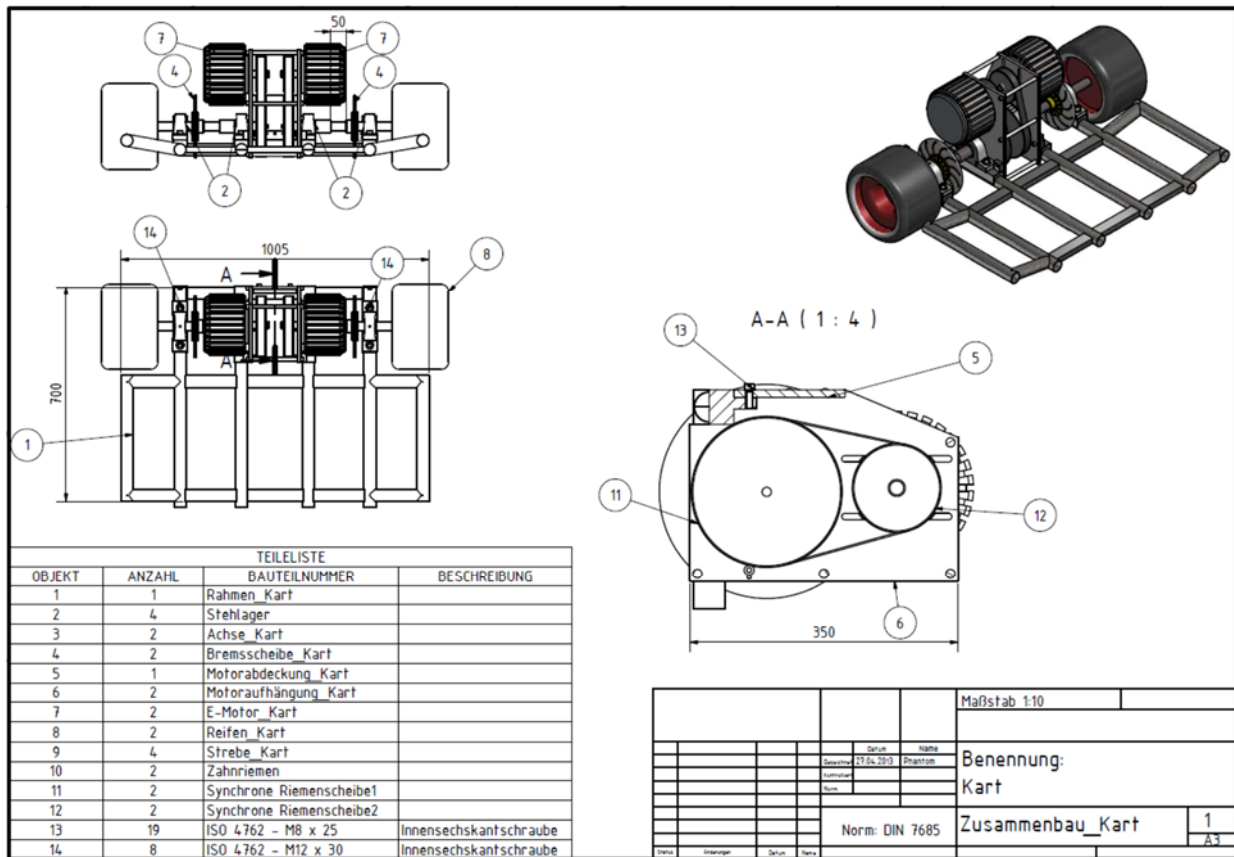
Fertigungsskizze des Heckaufbaus
